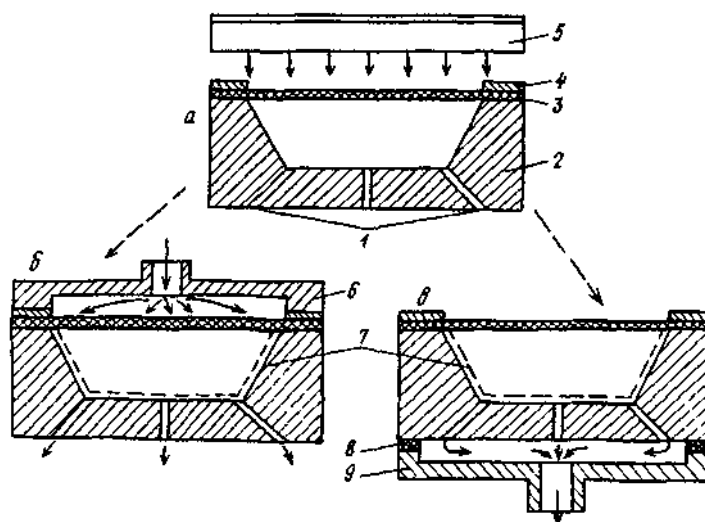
Схема негативного пневмо- и вакуумного формования изделий из листов термопластов: а – подогрев листа; б – пневмоформование; в – вакуумное формование; 1 – каналы для воздуха; 2 – форма; 3 – лист полимера; 4 – прижимная рамка; 5 – ИК-нагреватель; 6 – пневмостол; 7 – изделие; 8 – прокладка; 9 – вакуумный стол
